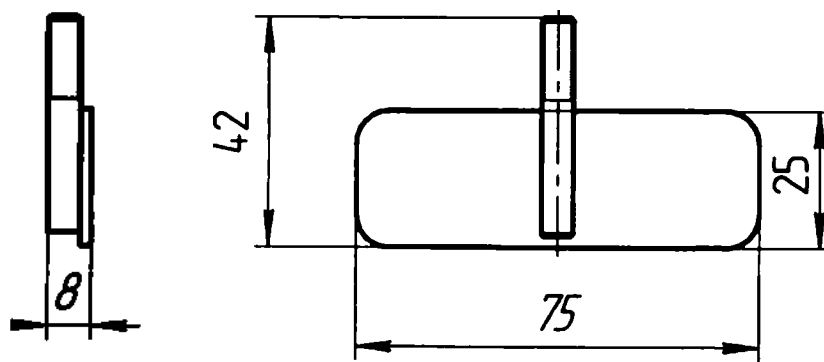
Габаритные размеры кронштейн крепления датчика движения
